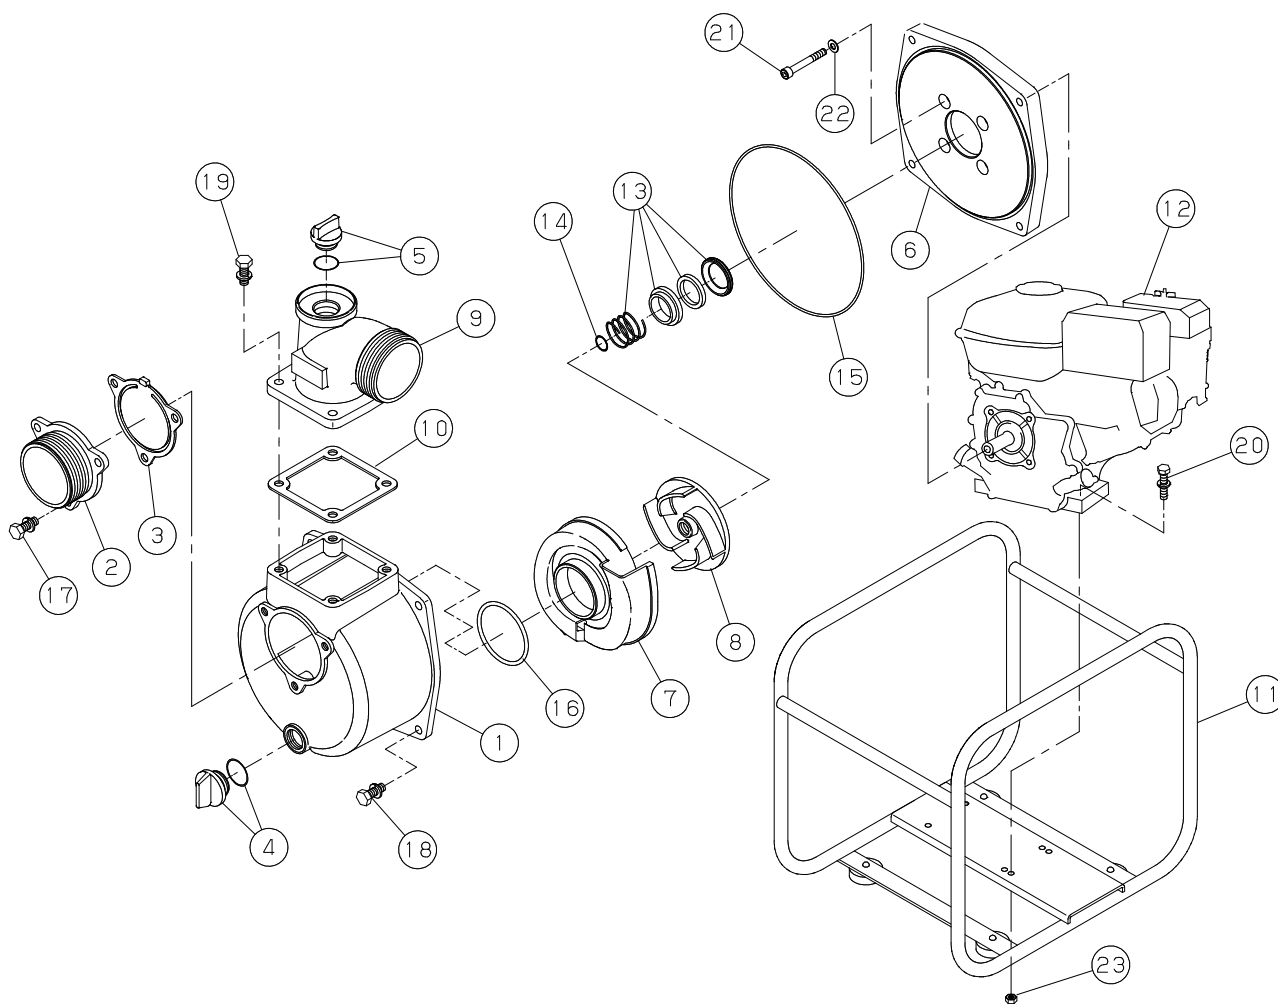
Illustration des pièces de rechange pour les pompes à moteur
